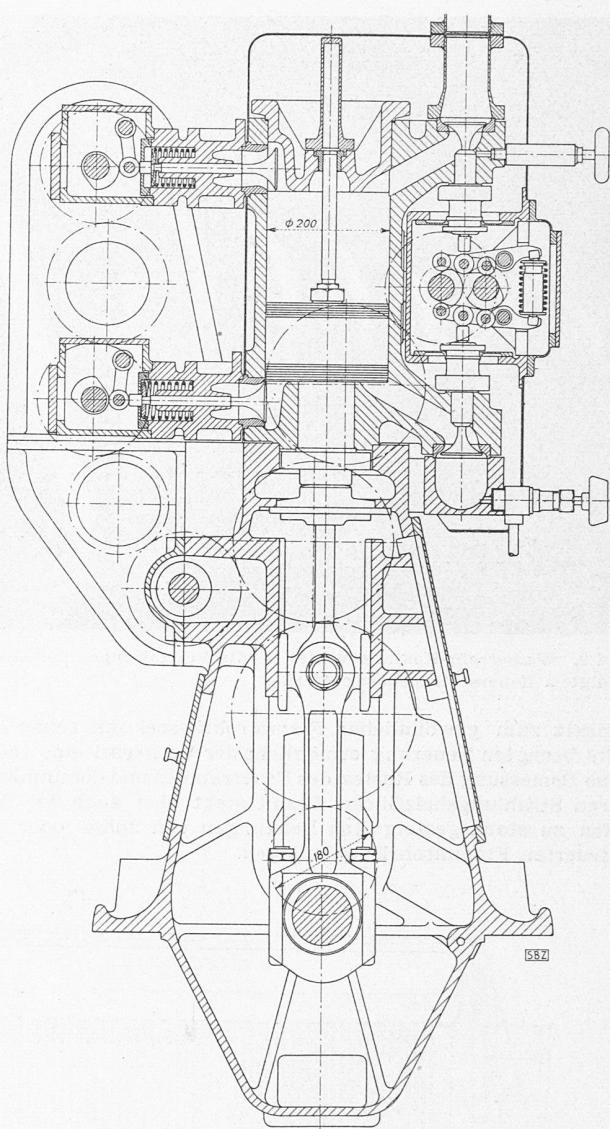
Schnellaufende Einzylinder-Dampfmaschine, Maßstab 1:12
